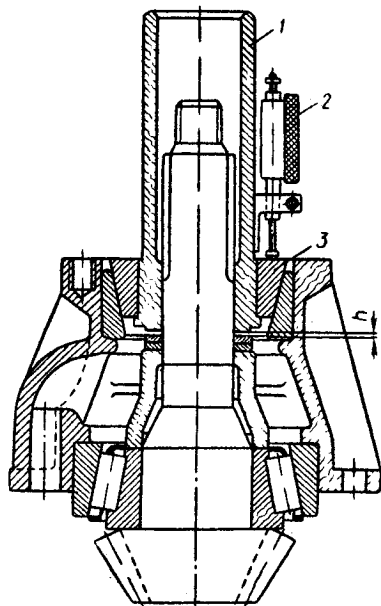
Пристрій для комплекту регулювальних шайб підшипників вала ведучої конічної шестірні
